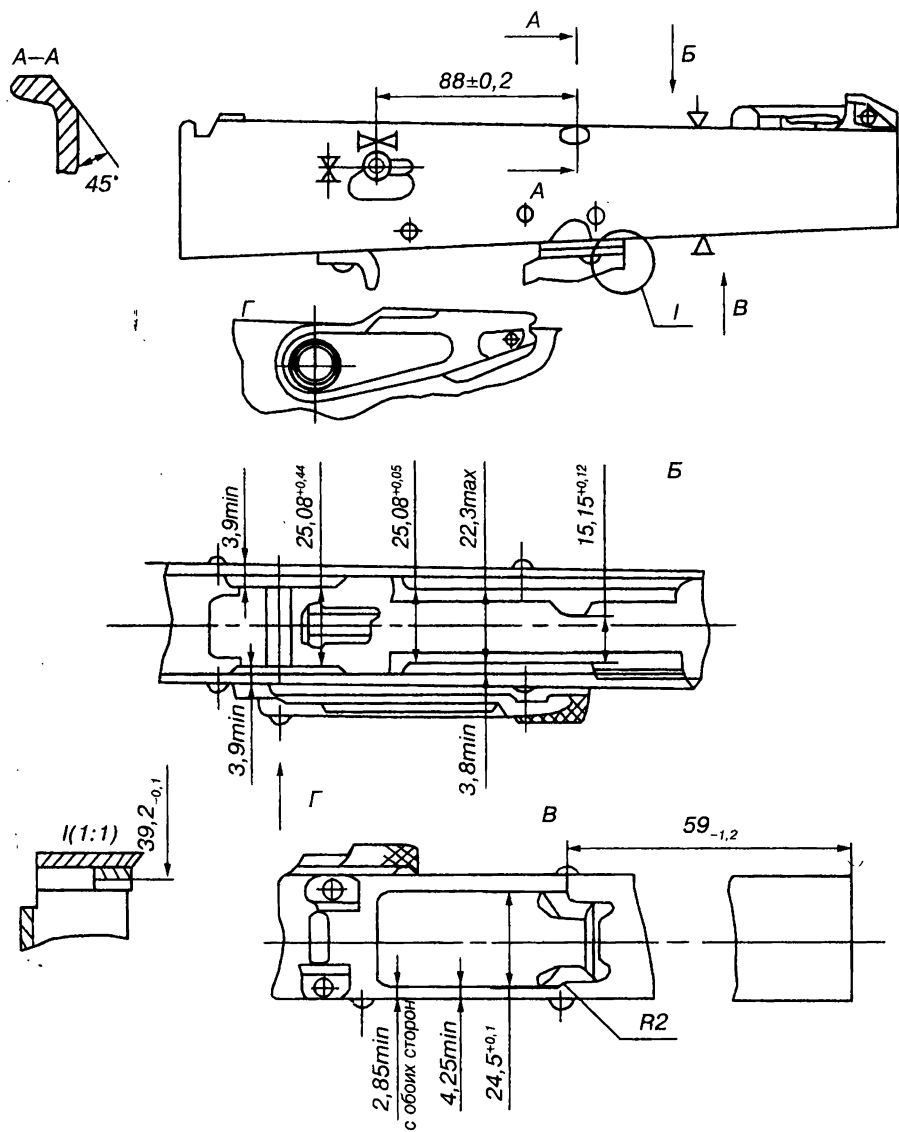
Установка переводчика огня, фрезерование и доводка поверхностей
